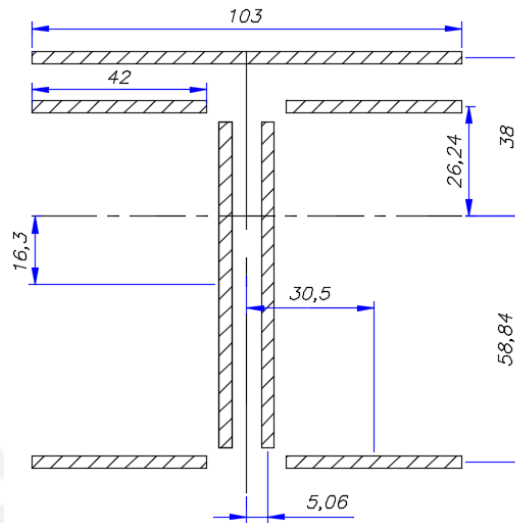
Dimensiones generales de la unión soldada y su centroide.
